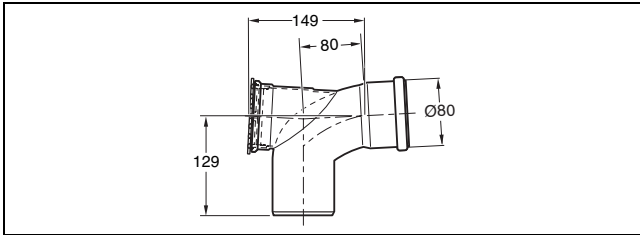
Bogen mit Prüföffnung lang (Maße in mm)
